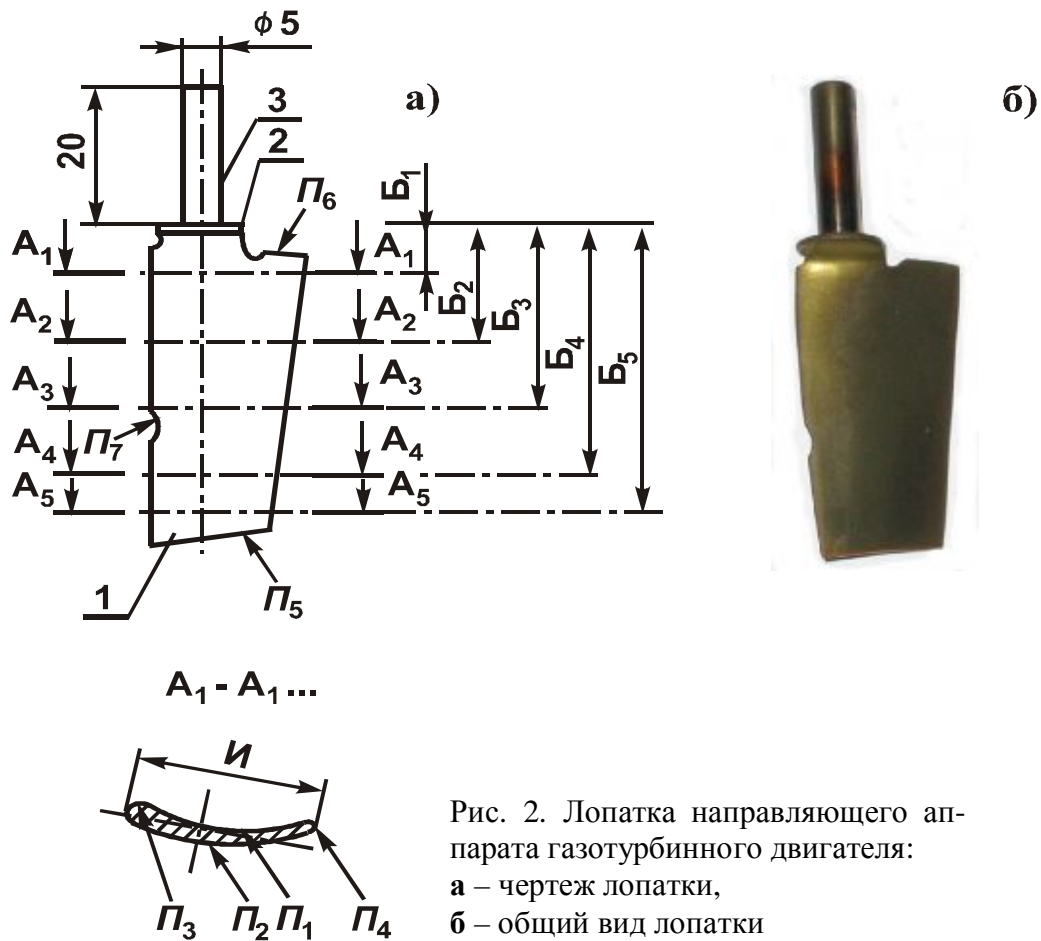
Лопатка направляющего аппарата газотурбинного двигателя:
